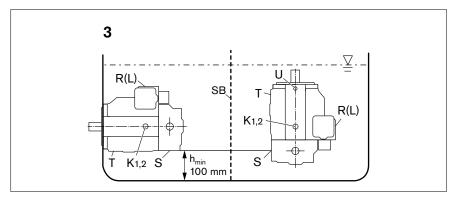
Montaje en tanque con posición de montaje horizontal y vertical 3
